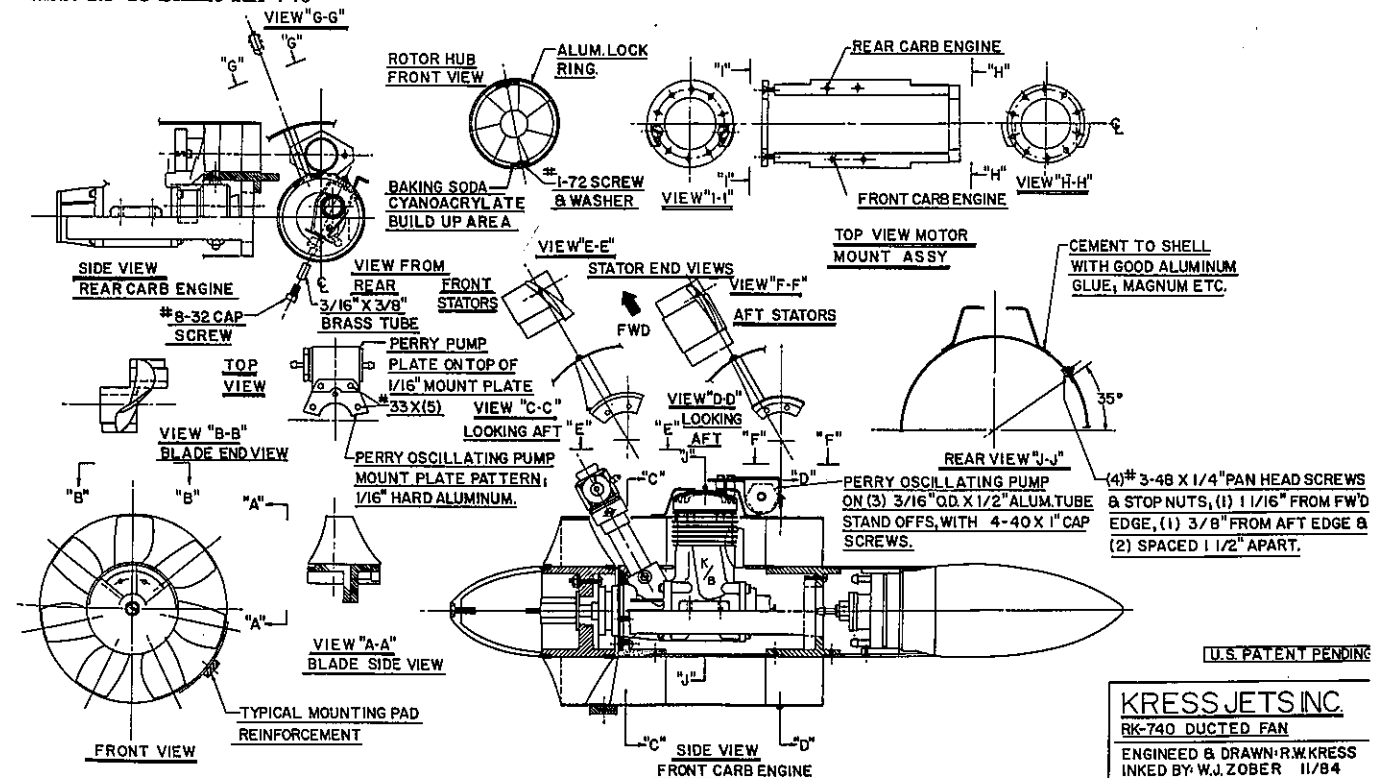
Bauteile des Kress RK-740 Impellers
